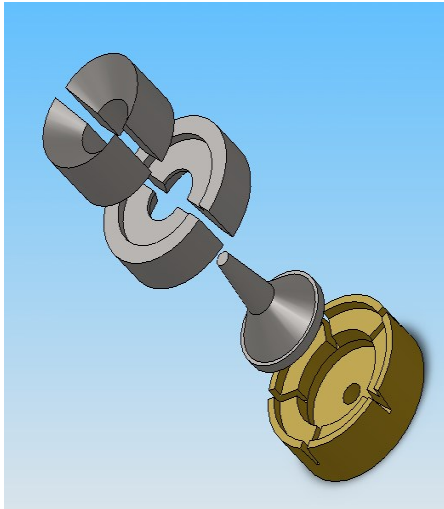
Vista explodida dos componentes do molde, mostrada em projeção isométrica, concebida em SolidWorks, para fabricação da arruela Belleville.
